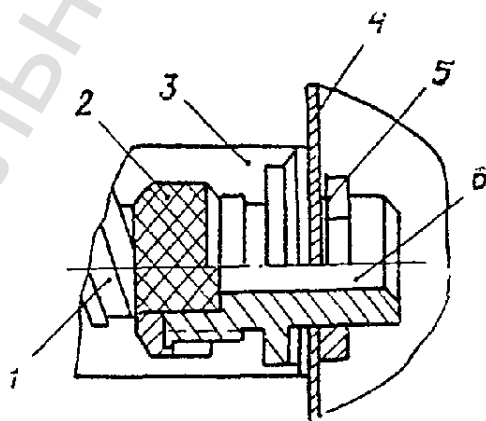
Крепление металлорукава к клеммной коробке с помощью штуцера:
